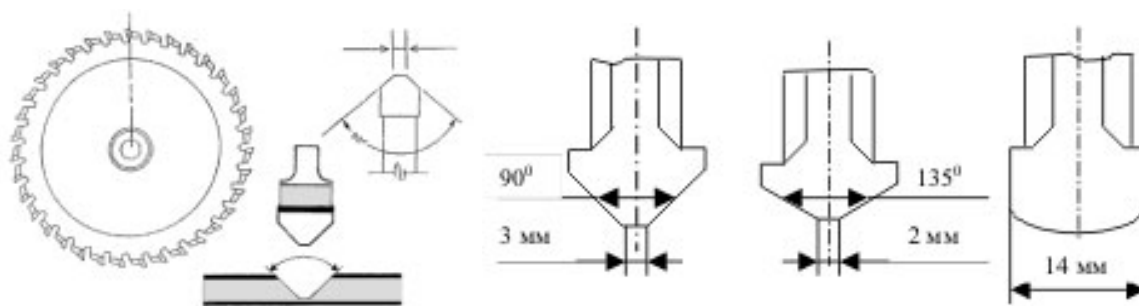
Типи дискових фрез для обробки АКП
